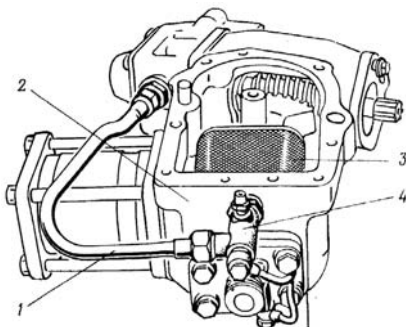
Снятие трубки подвода масла от распределителя: 1 — трубка подвода масла; 2 — корпус ГУРа; 3 — сетчатый фильтр; 4 — редукционный клапан.
